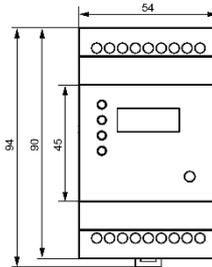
Габаритные размеры прибора Рисунок 2 – Монтаж прибора на DIN-рейку
